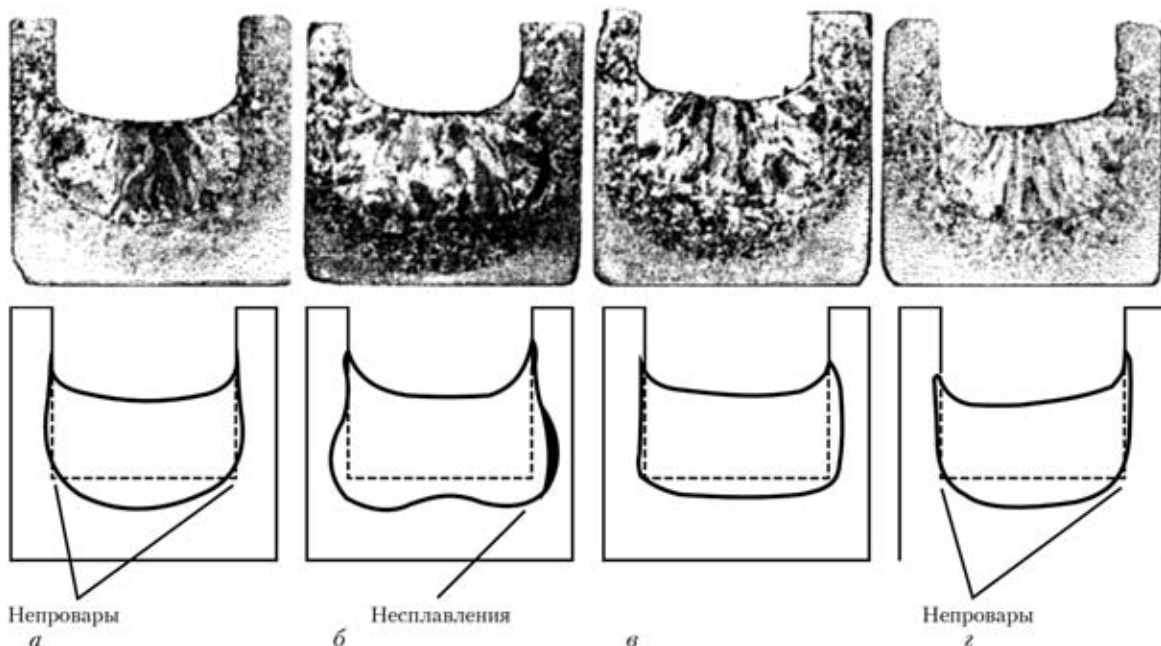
Макрошлифы валиков, полученных сваркой в узкий зазор (вверху), и схемы форм проваров (внизу): *a* — валик, полученный без управляющего магнитного поля; *б* — $b_в < b_н$; *в* — $b_в = b_н$; *г* — $b_в > b_н$
